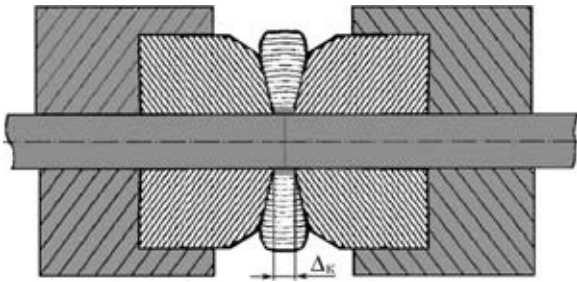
Схема формирования сварного соединения с конечным зазором Δ_k
